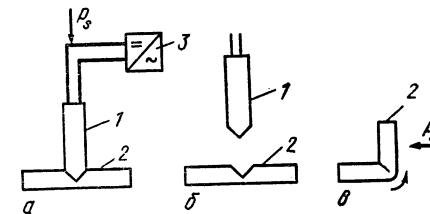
Принцип сварки тавровых и угловых соединений:
